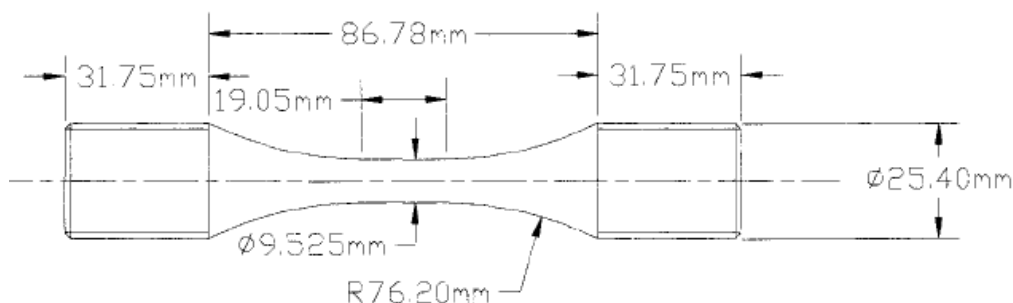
Géométrie des éprouvettes de fatigue cylindrique
